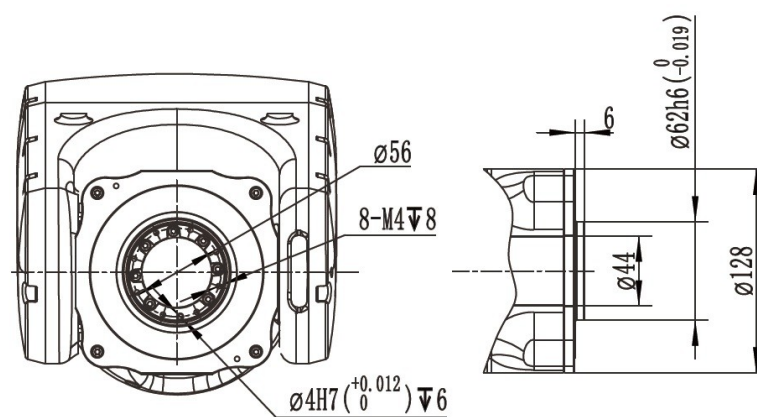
Размеры фланца CRP-RH18-20 (W).
